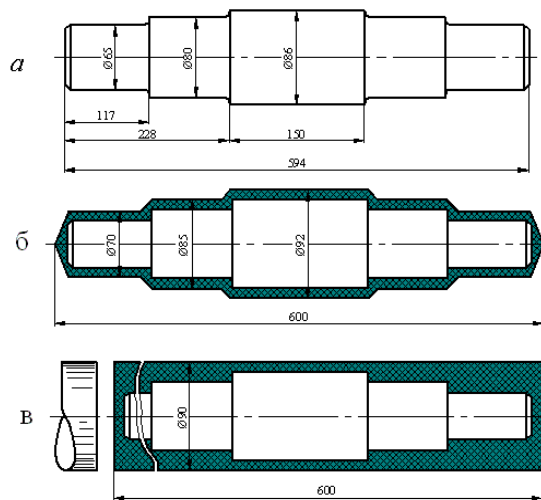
Вал ступінчастий: а – деталь; б – штампована поковка; в – заготовка з гарячекатаного прокату
